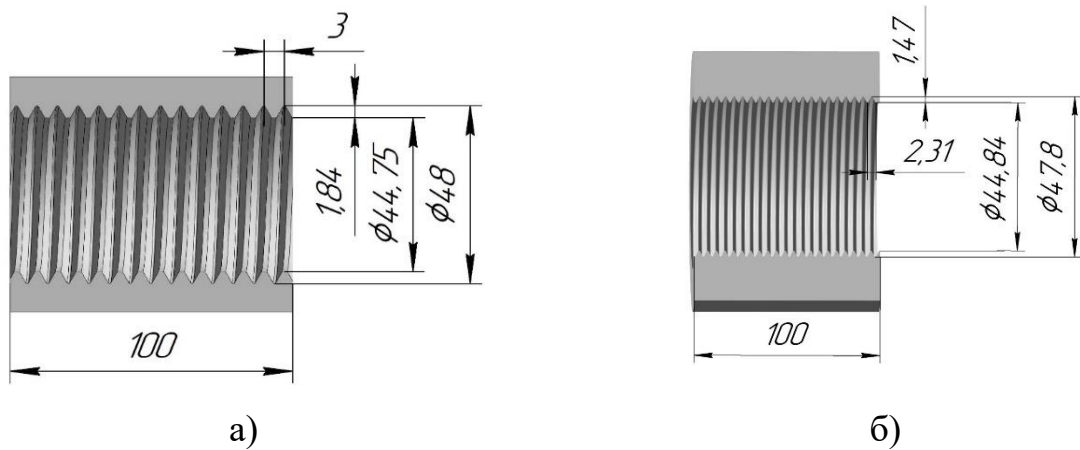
Різьова частина: а) муфти з'єднувальної; б) гайки круглої
